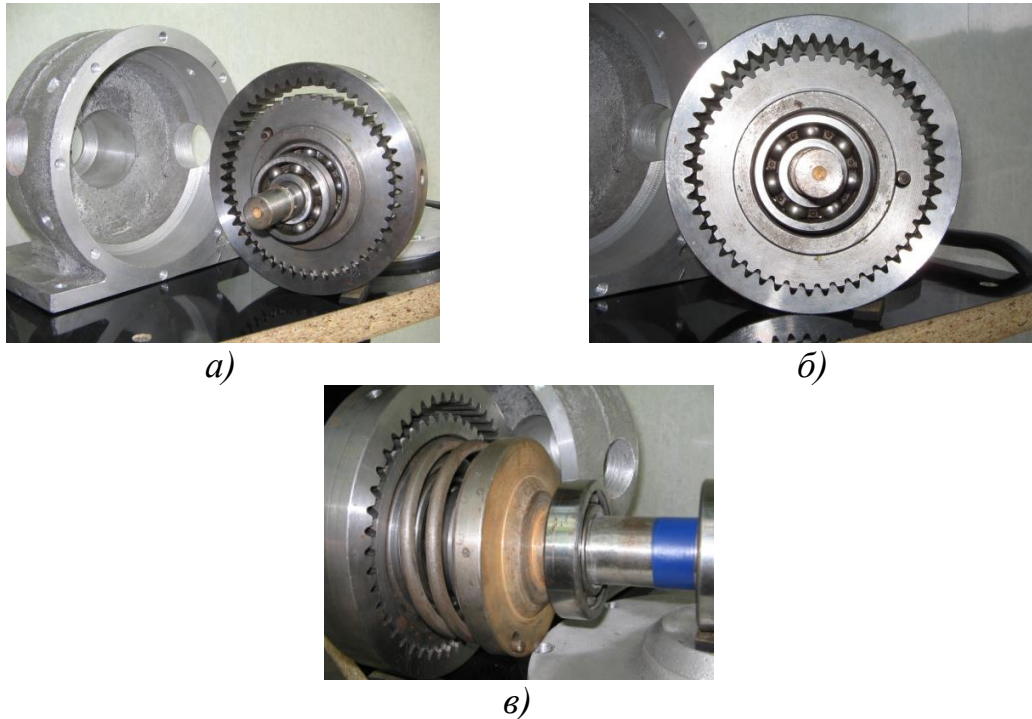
Сполучення елементів конструкції пружньо-хвильового редуктора
